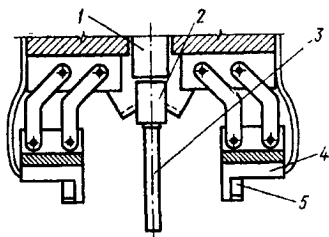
Варіант конструкції захоплювача із розміщенням датчиків та інформаційного щупа: 1 – висувний елемент; 2 – силовий датчик; 3 – щуп; 4 – губки захоплювача; 5 – фотодалькоміри
